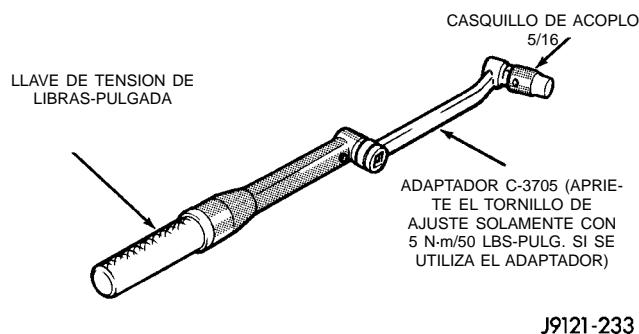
Herramienta adaptadora de ajuste de la cinta
